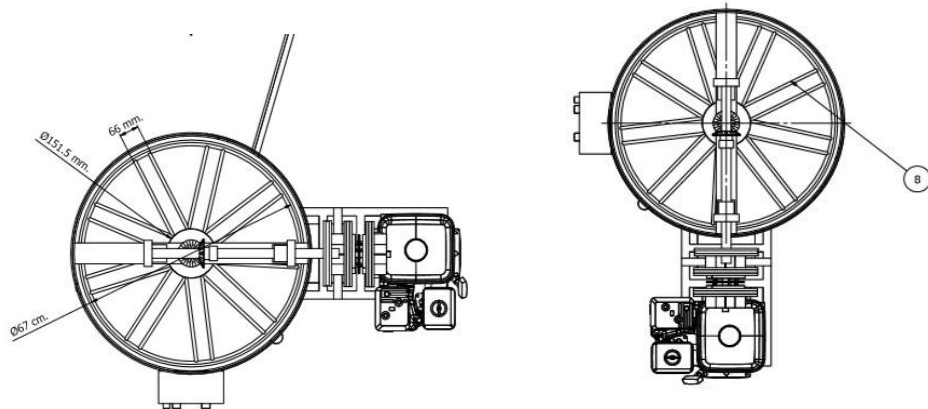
แสดงการออกแบบเครื่องสไลด์น้ำผึ้ง Assembly Drawing
